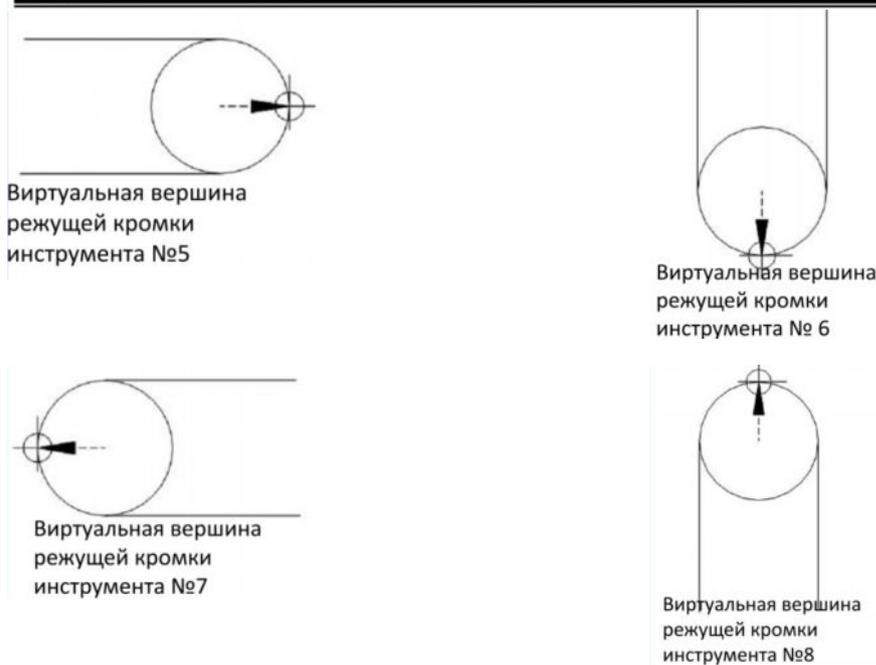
Номера виртуальной вершины режущей кромки инструмента в системе координат переднего держателя инструмента
